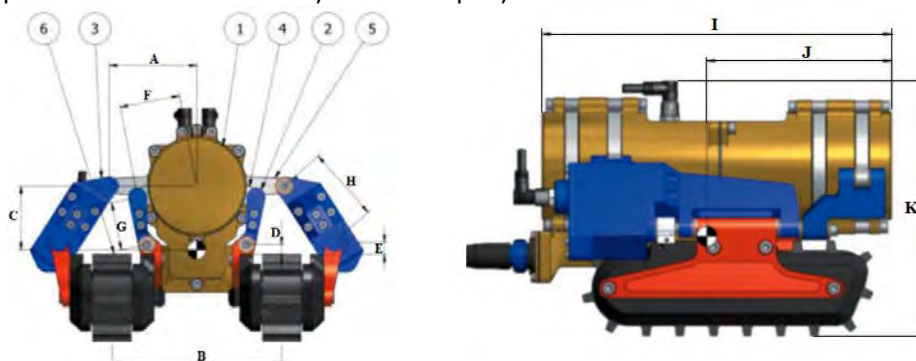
Soluția constructivă cu șenile a robotului de inspecție model CAD: 1 – șasiu robot, 2 - braț față, 3 - braț spate, 4 - inel rotativ față, 5 - inel rotativ spate, 6 – modul de acționare șenile.
